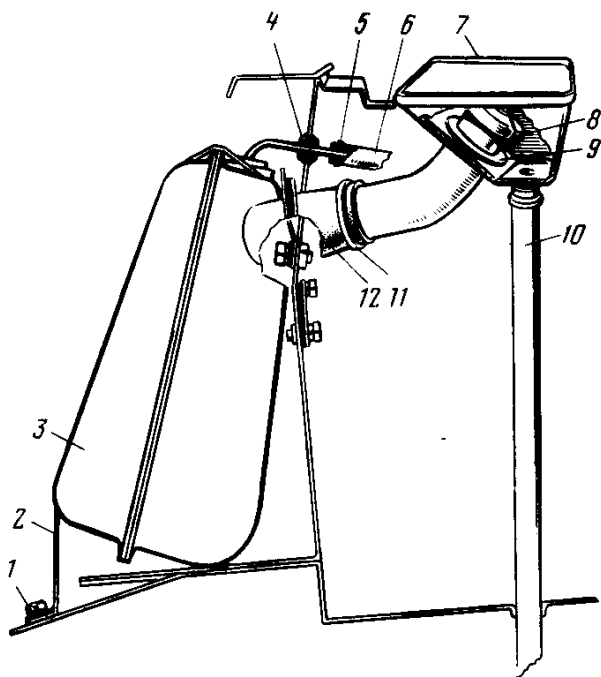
Топливный бак и его крепление к кузову: 1 — болт; 2, 5, 11 — хомуты; 3 — топливный бак; 4, 9, 12 — уплотнители; 6 — топливопровод; 7 — лоток; 8 — пробка заливного отверстия; 10 — сливной шланг
